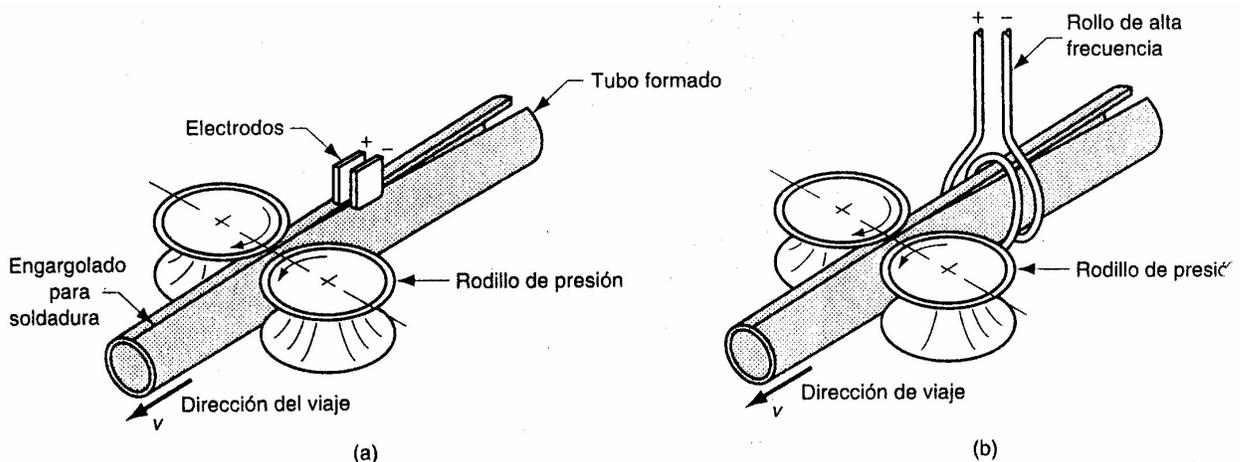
Soldadura de engargolados de tubos mediante (a) soldadura por resistencia de alta frecuencia y (b) soldadura por inducción de alta frecuencia.
